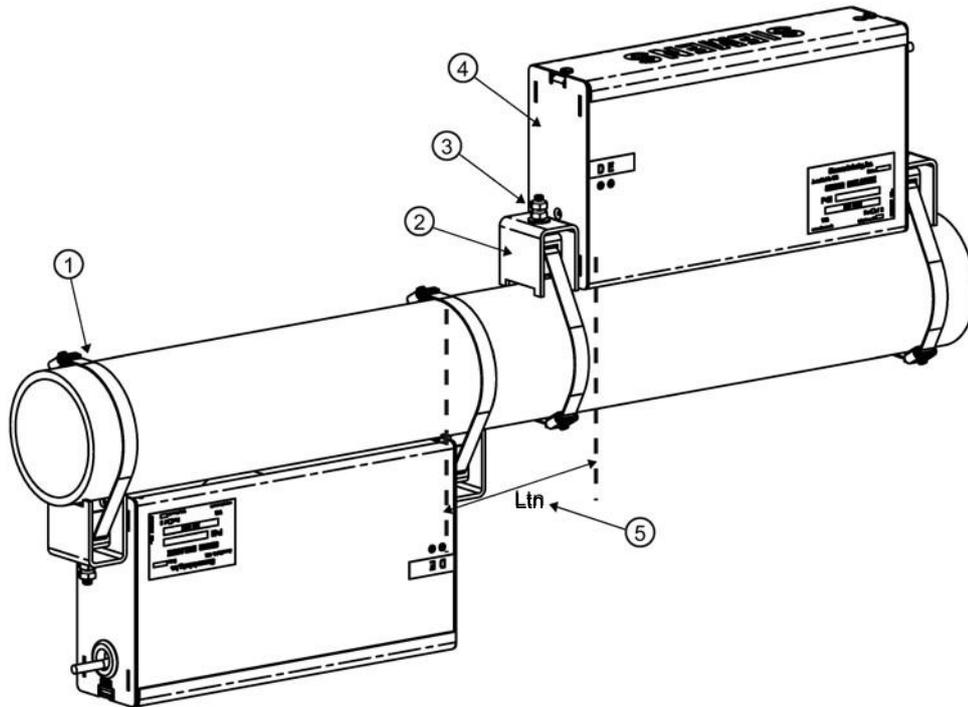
Двойной корпус с установленным высокоточным датчиком
